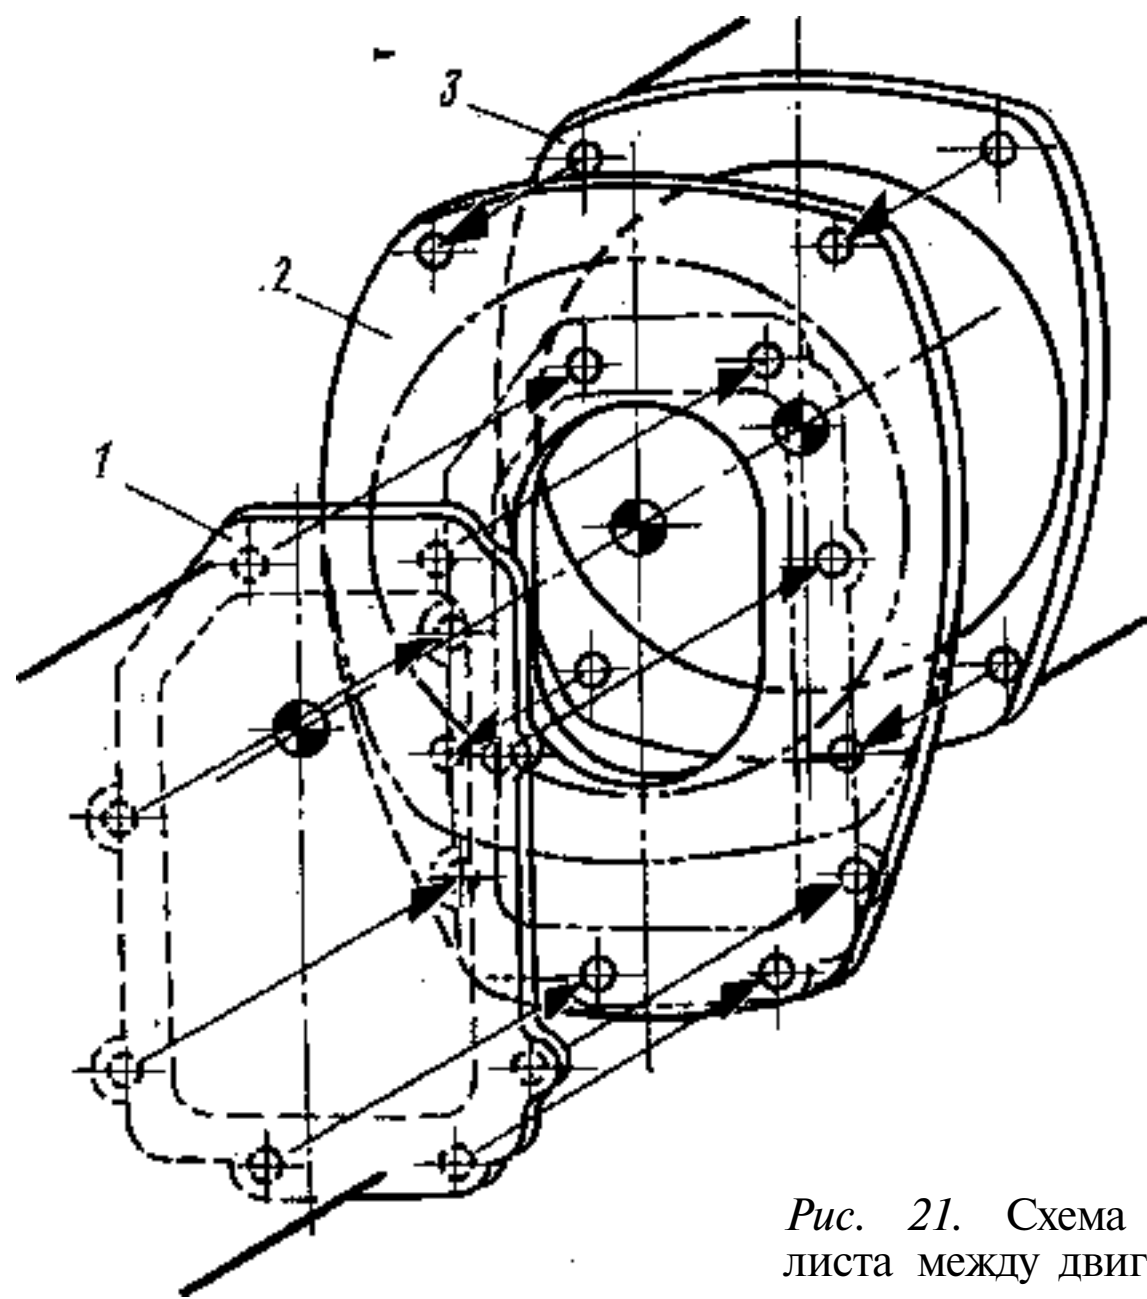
Схема установки промежуточного листа между двигателем и коробкой передач:
